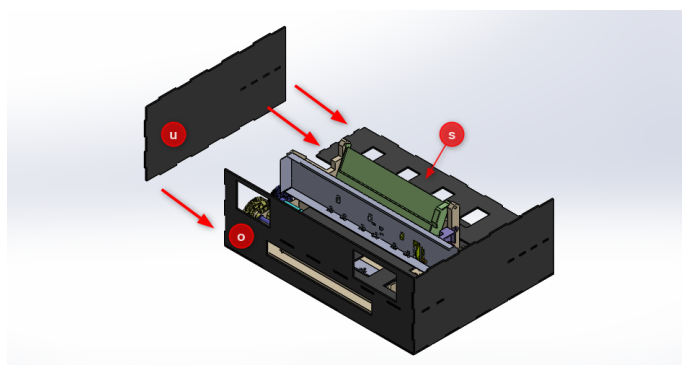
Montaje de la carcaza lateral izquierda (u)
